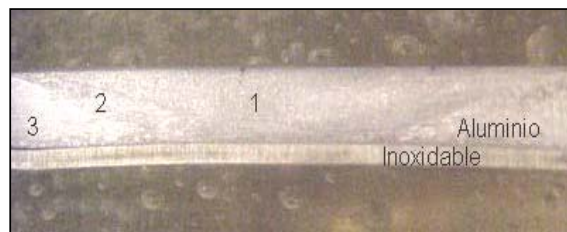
Macrografía de una sección transversal a la dirección de soldadura de una probeta Al-SS atacada químicamente. [6]
